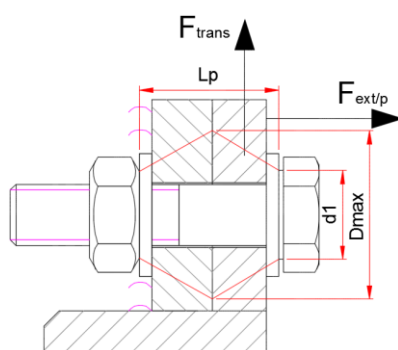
Unión atornillada eje S1 - caja para engranajes.
